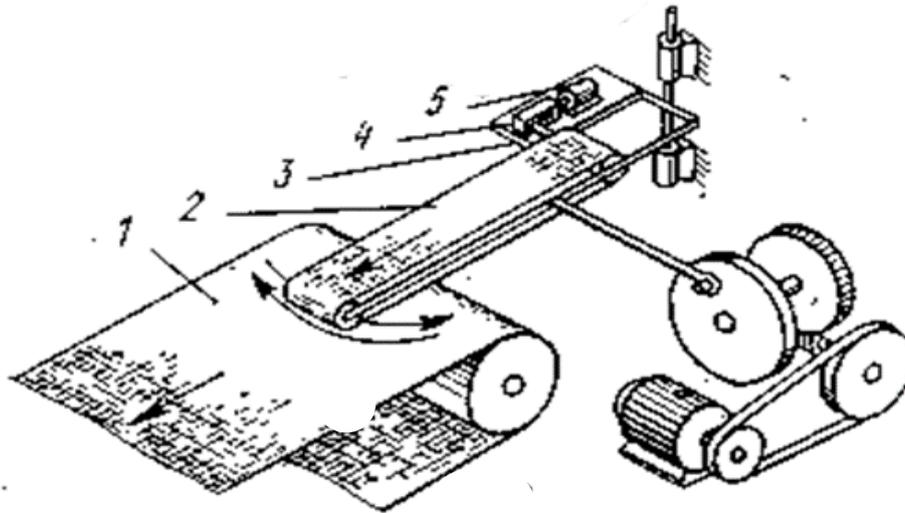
Раскладчики короткорезанных изделий с качающейся трубой с качающимся транспортом:
